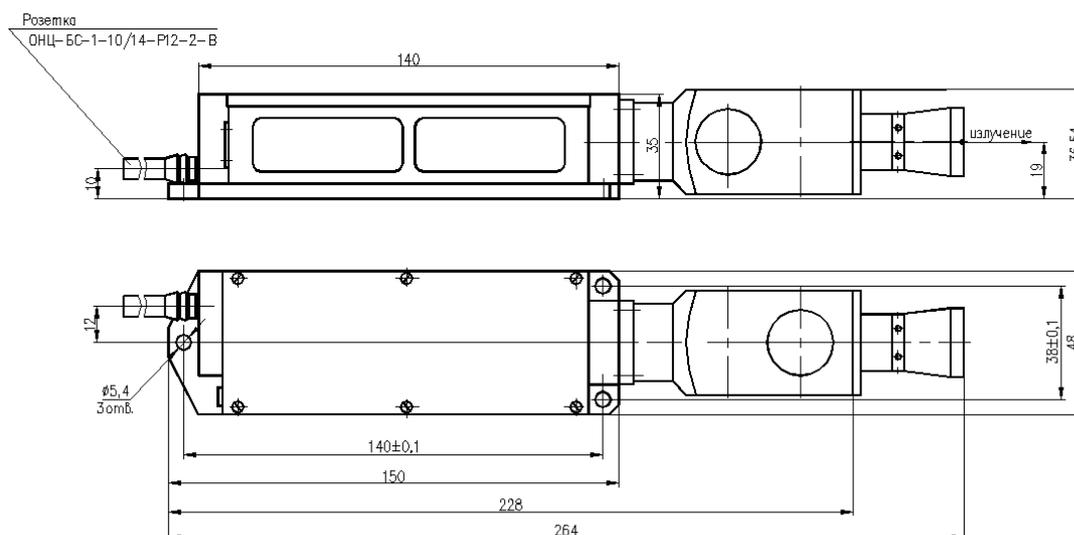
Габаритный чертеж излучателя PC-01GM
